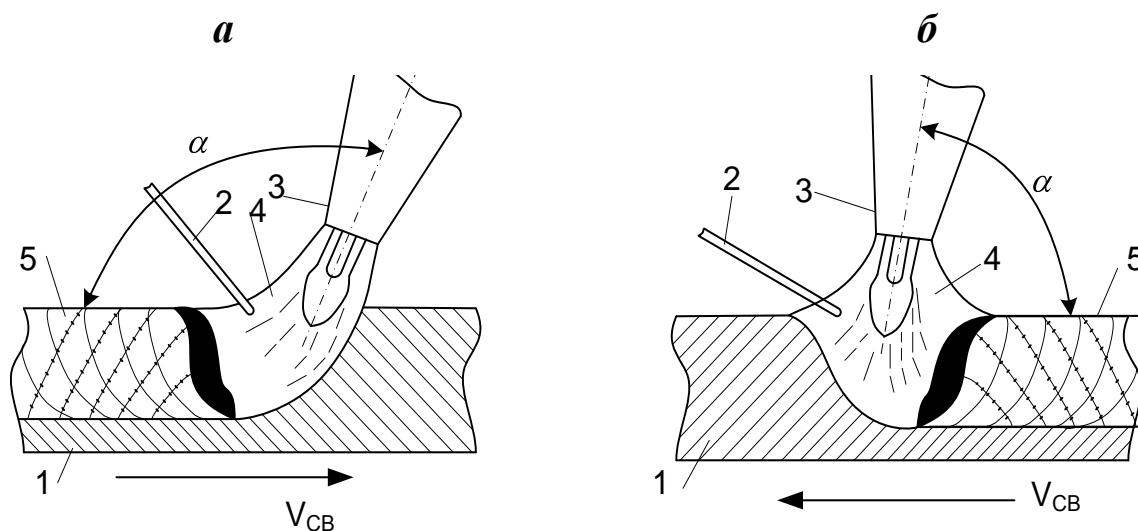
Схема газовой сварки правым (а) и левым (б) способом:
